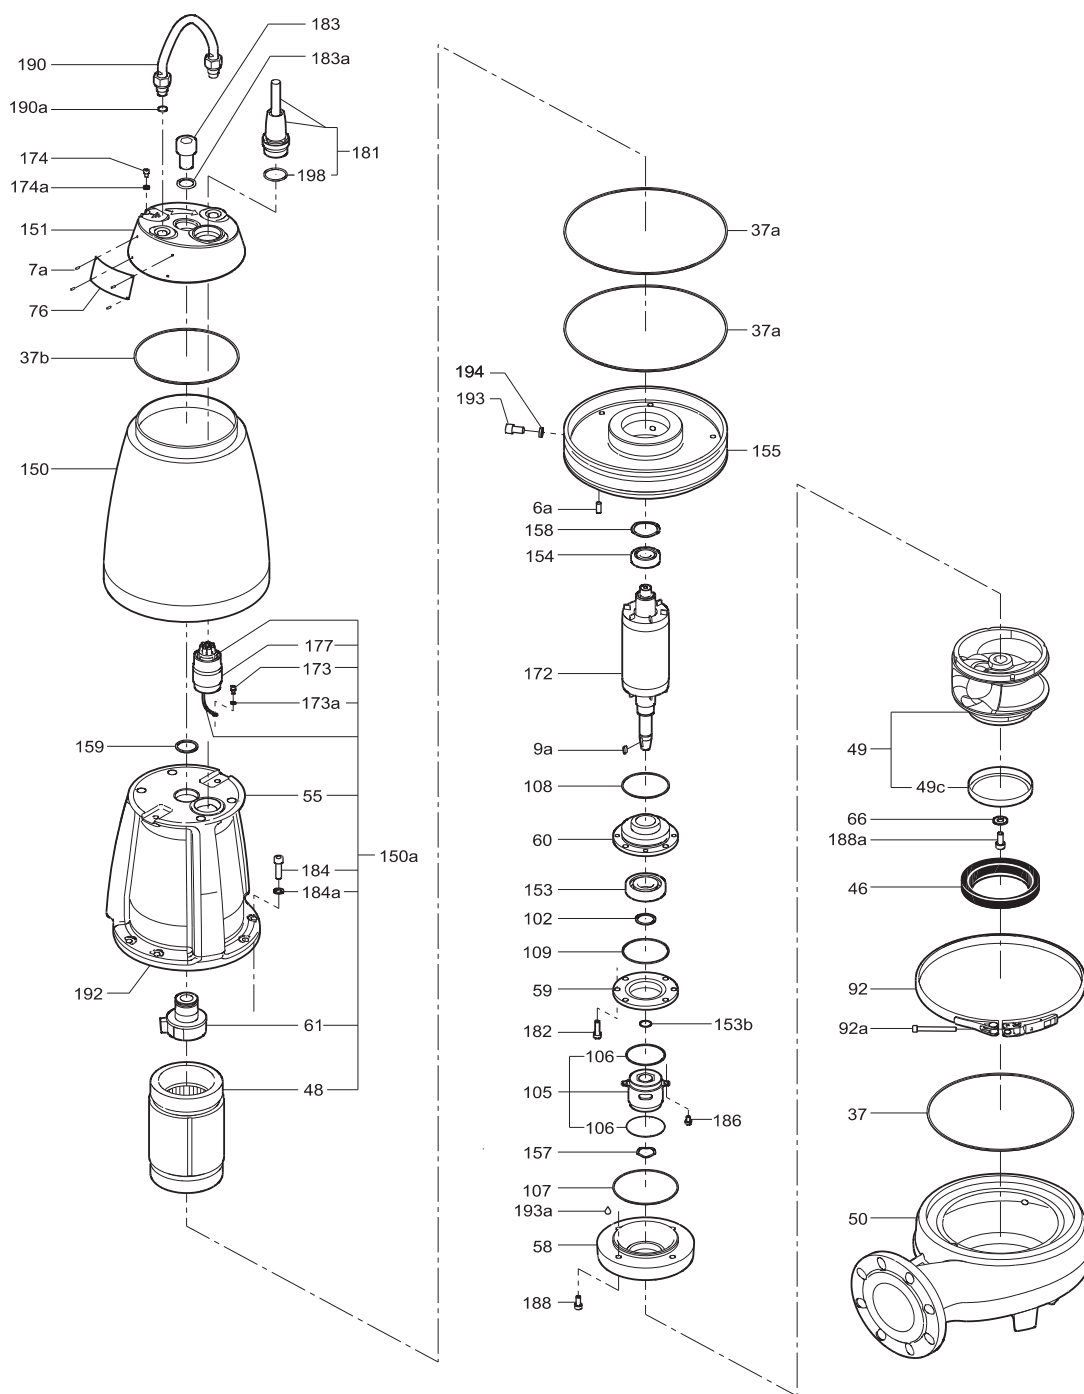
Детализовка насоса SE1 с одноканальным рабочим колесом типа S-tube
